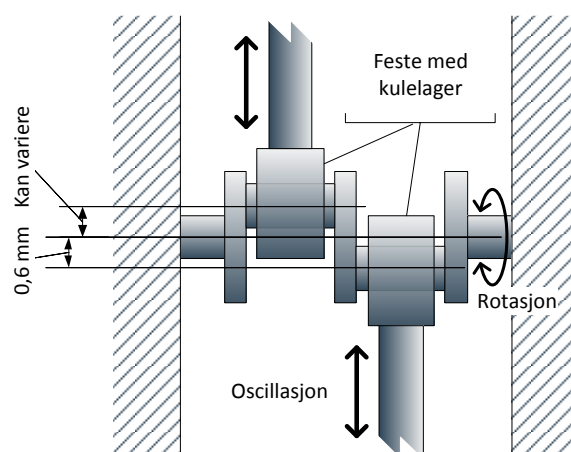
viser en veivaksel hvor en rotasjonsmotor driver veivakselen rundt, eventuelt en lineærmotor som driver én eller flere råder. Dette er en relativt god løsning for å sikre den oscillerende bevegelsen.
